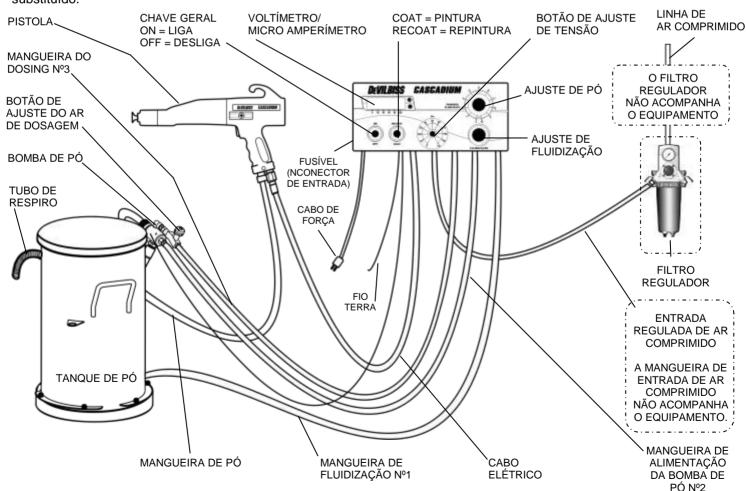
Instalação de um conjunto eletrostático de pintura a pó.
